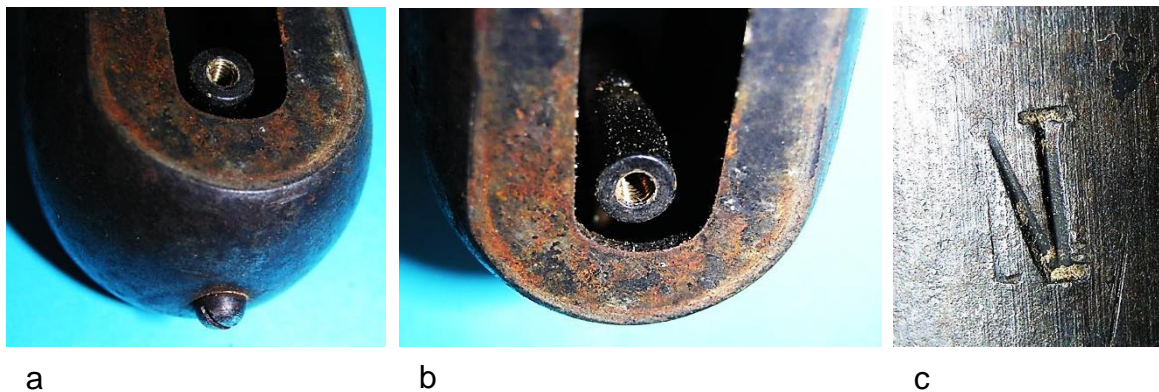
Montagehilfen: a) Befestigung der Gewindehülse am Magnetjoch, b) Position der Gewindehülse zur Befestigung der Pollückenbleche, c) Markierung des Nordpols auf einem Magnetschenkel
